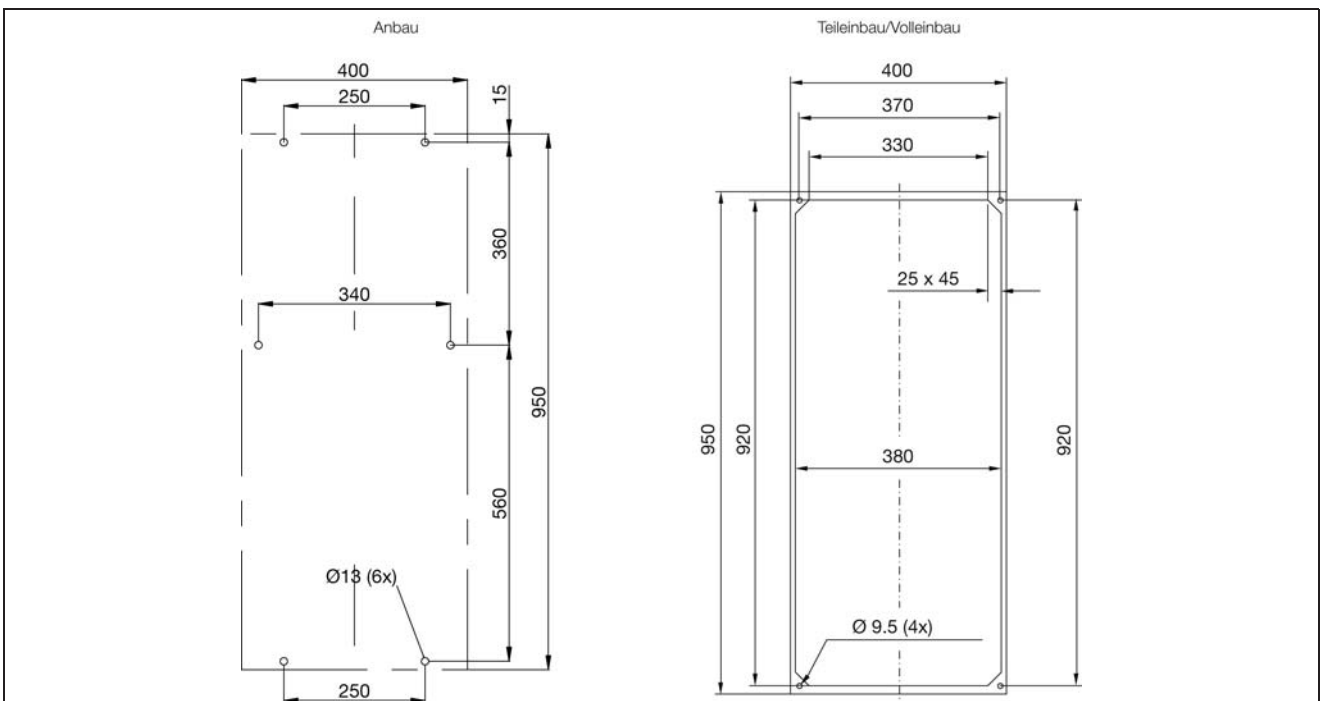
Montageausschnitt für Anbau/Teileinbau/Volleinbau
